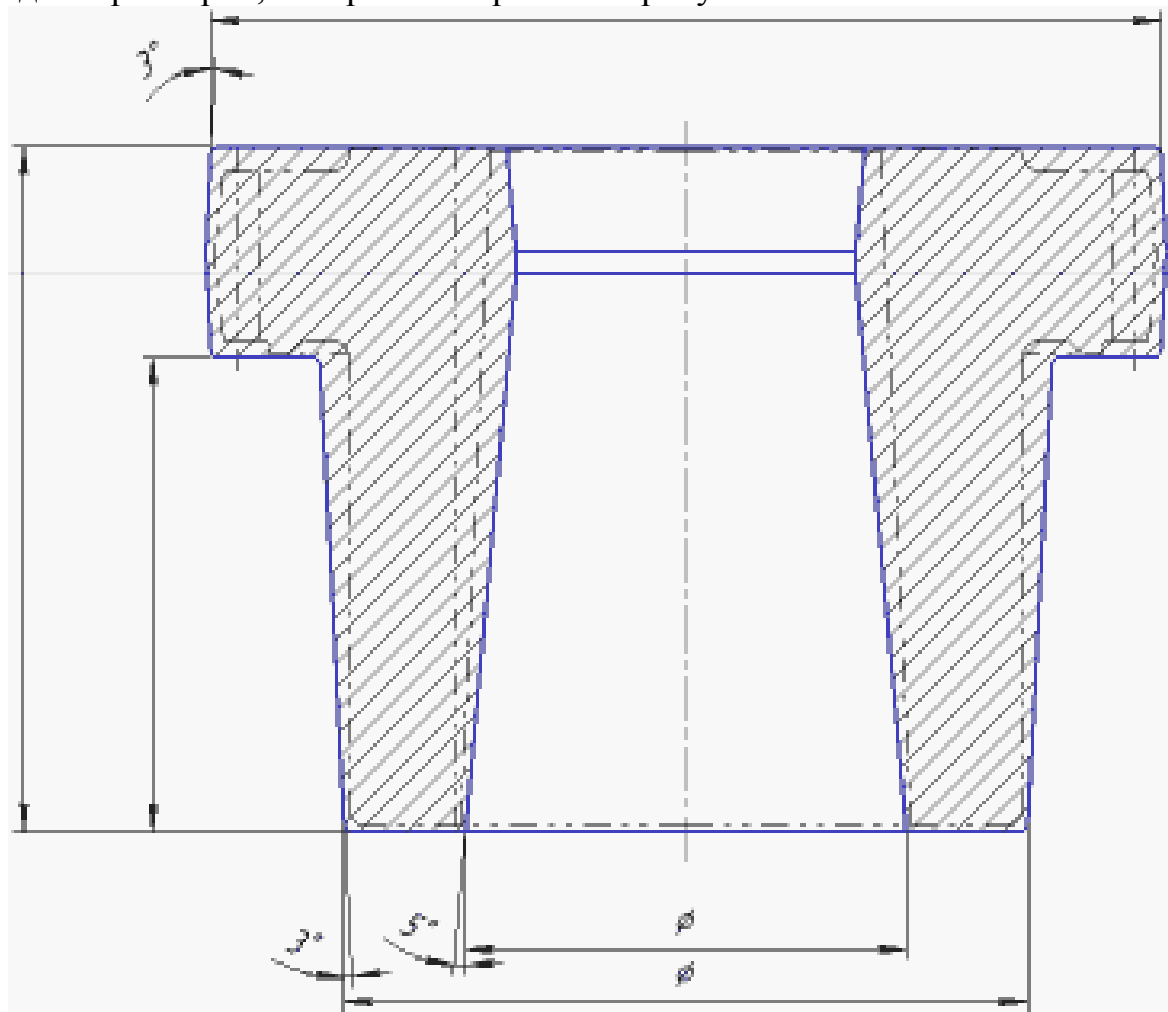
Исходная заготовка детали «Полумуфта зубчатая (левая)».
